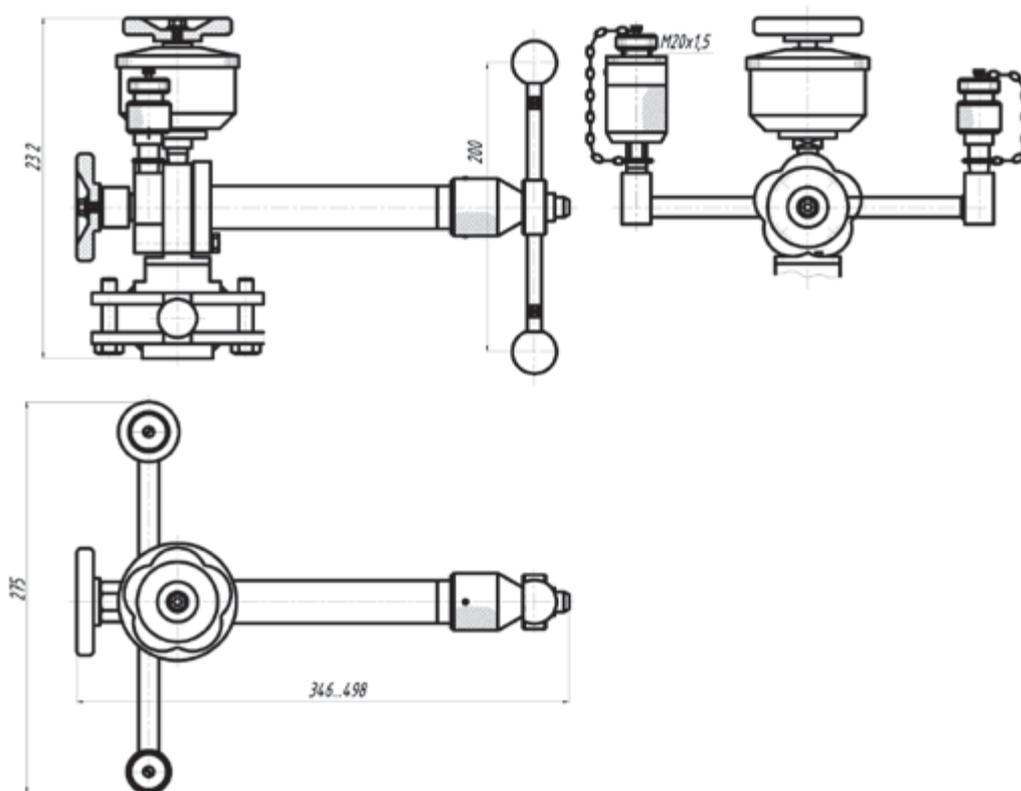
Габаритные размеры пресса универсального малогабаритного ПУМ 6
